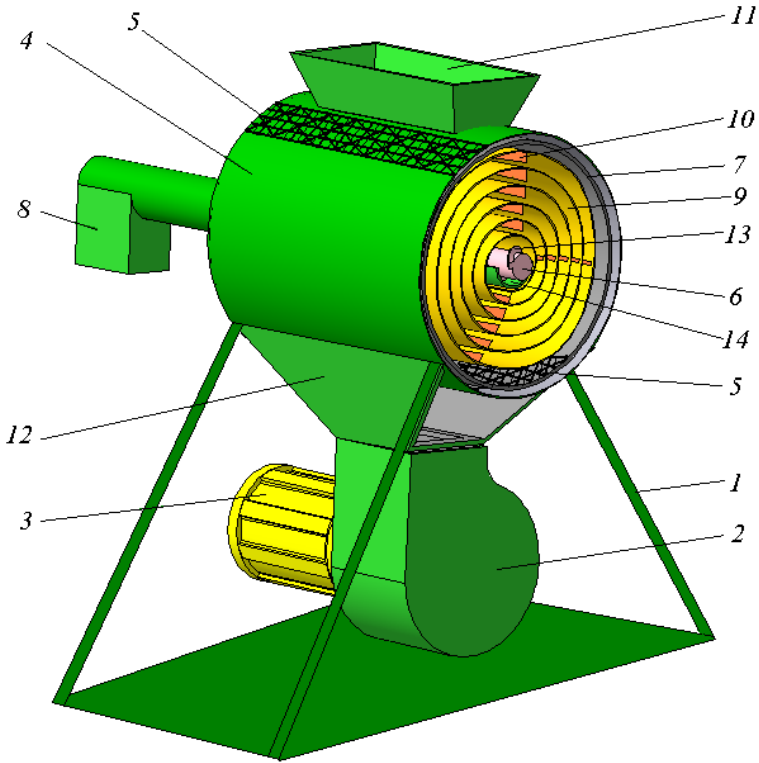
Схема барабанної сушарки: 1 – рама; 2 – вентилятор; 3 – електрокалорифер; 4 – циліндричний кожух; 5 – перфоровані вставки; 6 – приводний вал; 7 – сушильний барабан; 8 – вивантажувальний пристрій; 9 – перфорована поверхня; 10 – полицка; 11 – завантажувальний отвір; 12 – дифузор; 13 – вивантажувальний шнек; 14 – жолоб
